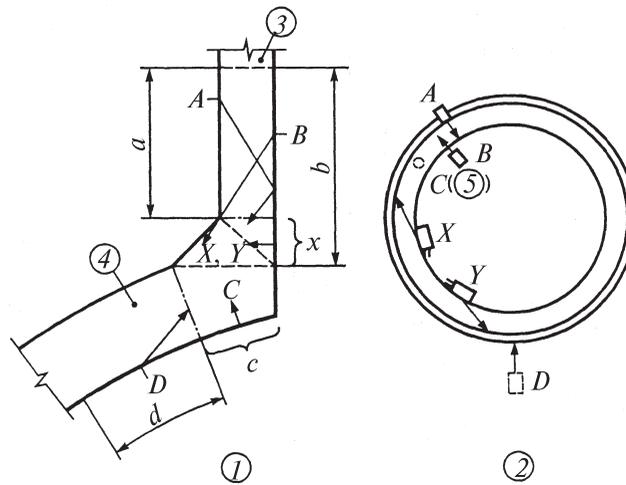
Сварное соединение патрубка (насадное):
